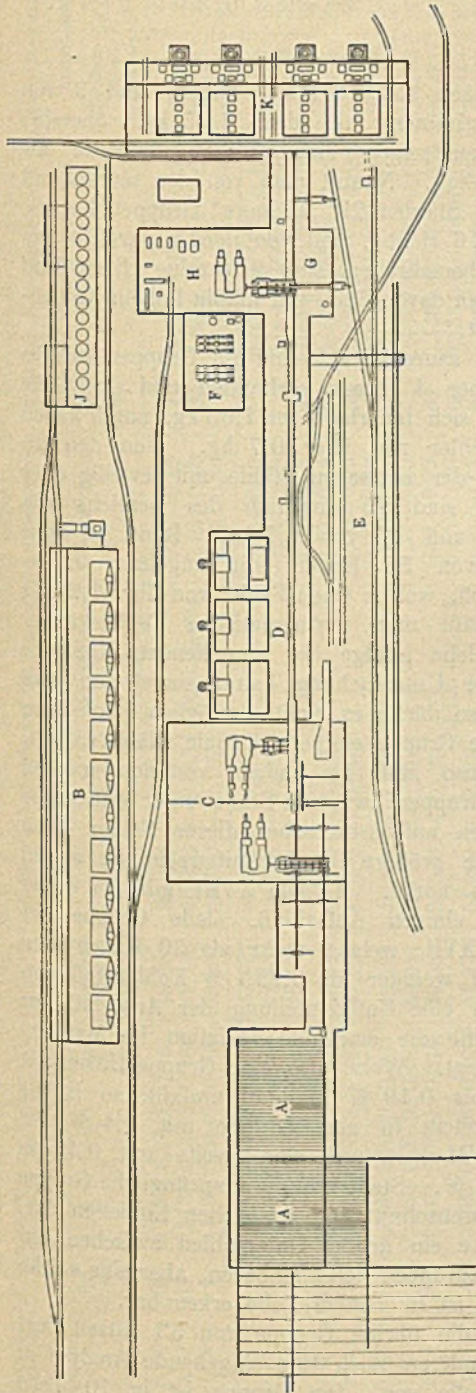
Lageplan des Konstruktionseisen-Walzwerks.
